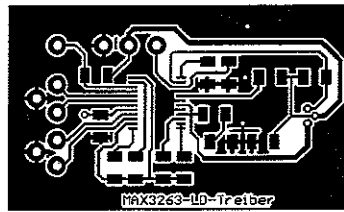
Für den MAX3263 wird ein zweiseitiges Platinenlayout benutzt. Die Bestückung erfolgt auf der hier angezeigten Seite.
